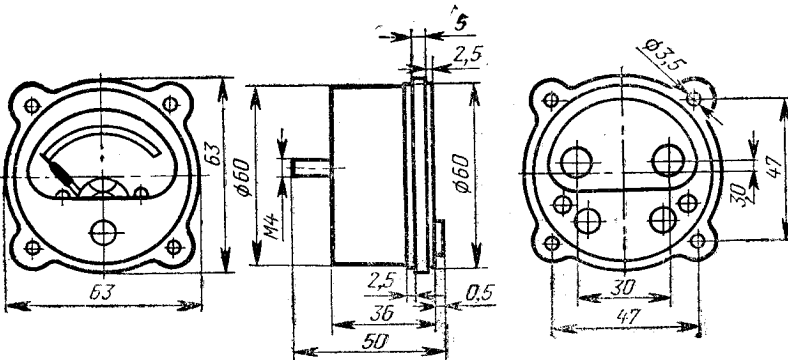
Габаритный чертеж прибора типа Ц24М.
